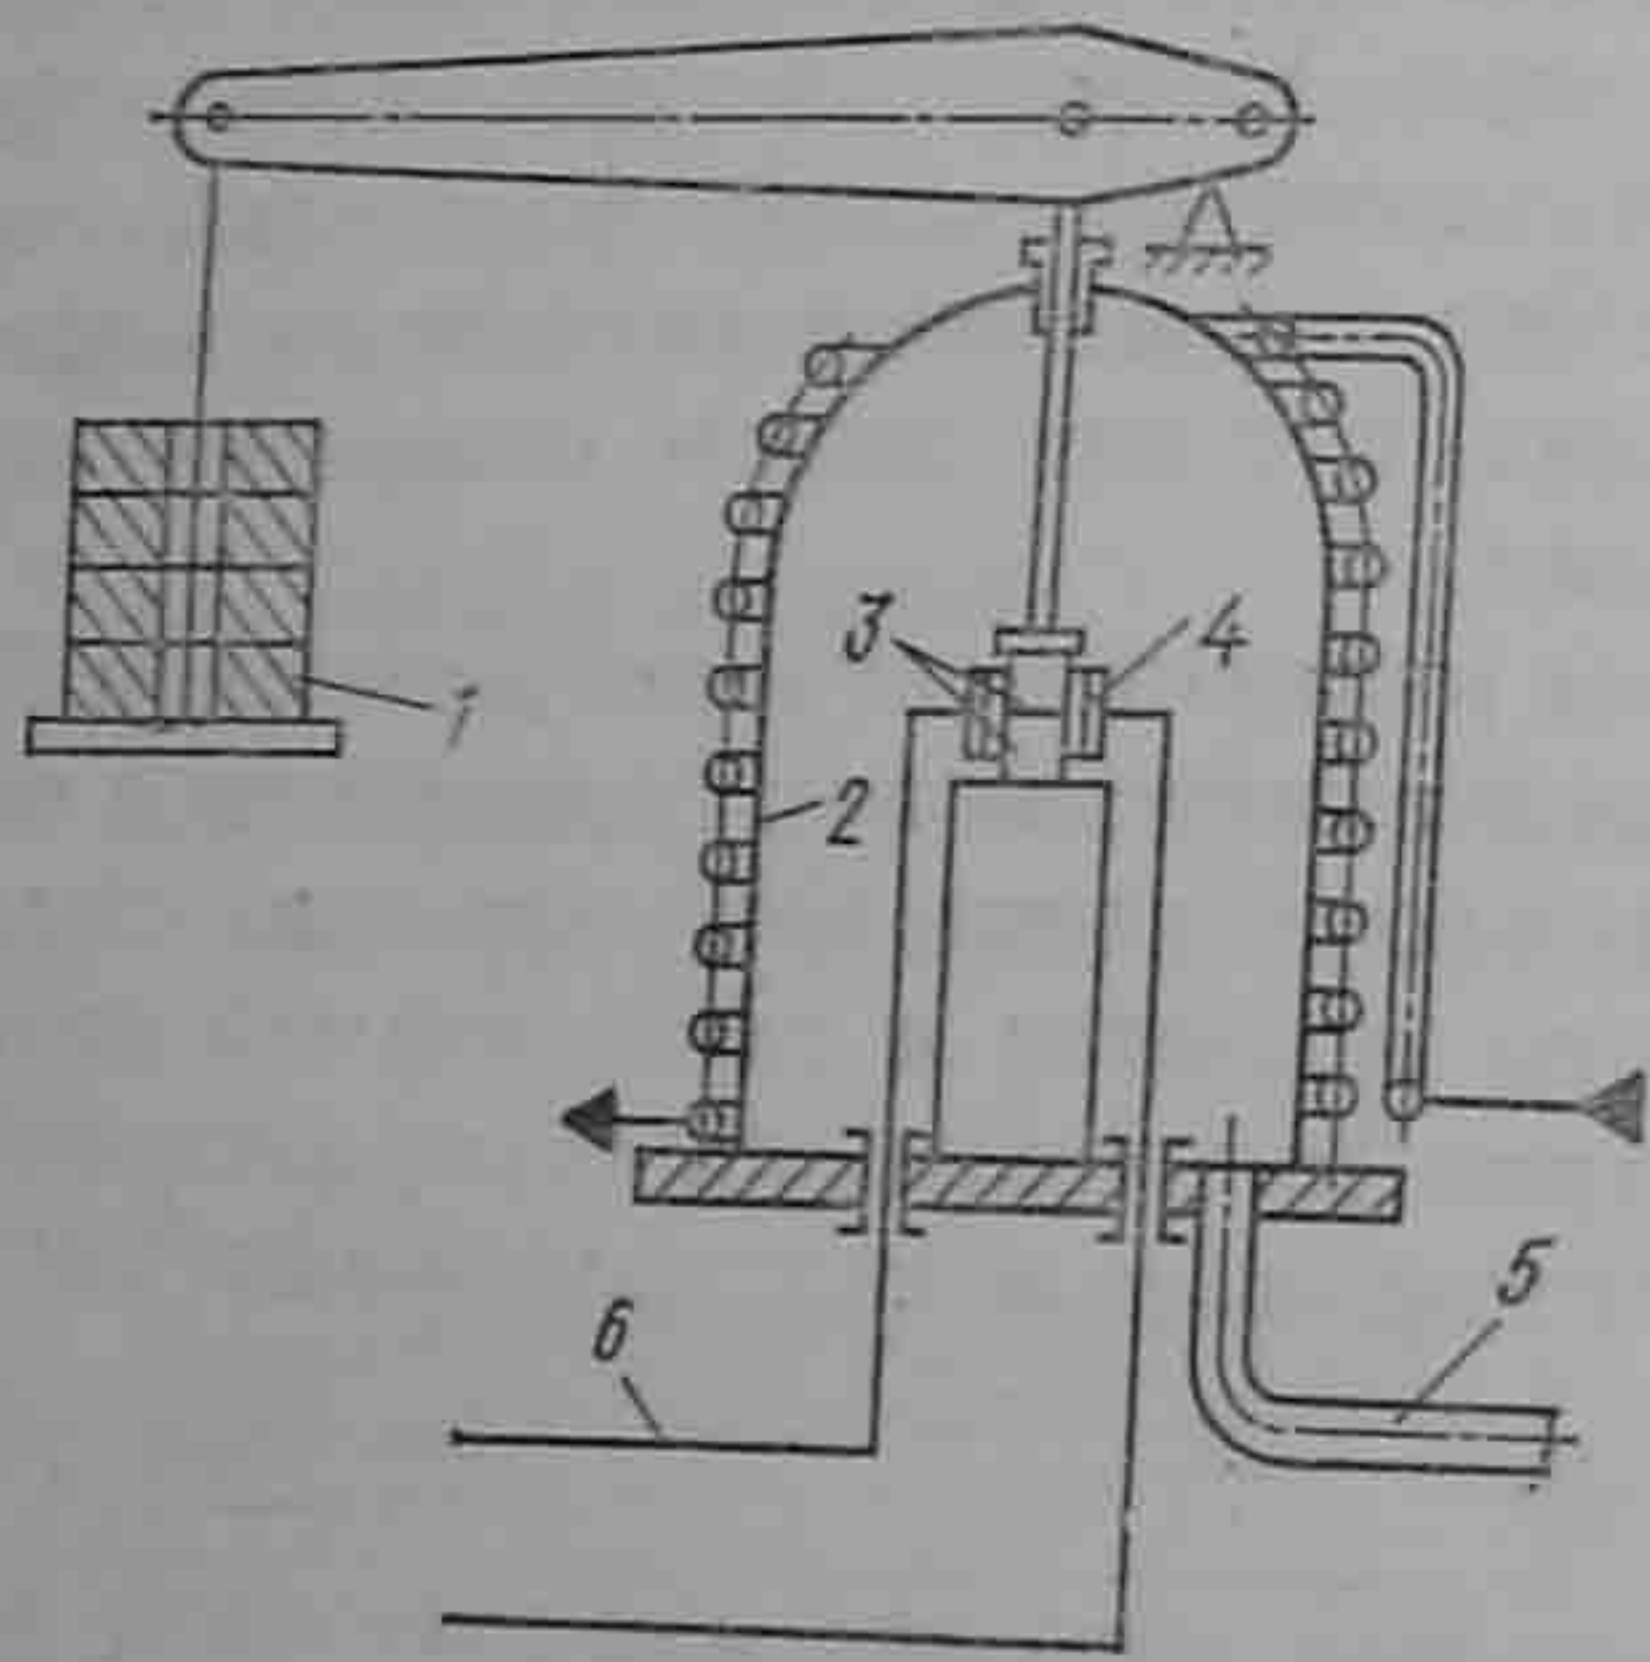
Принципиальная схема диффузионной сварки в вакууме
